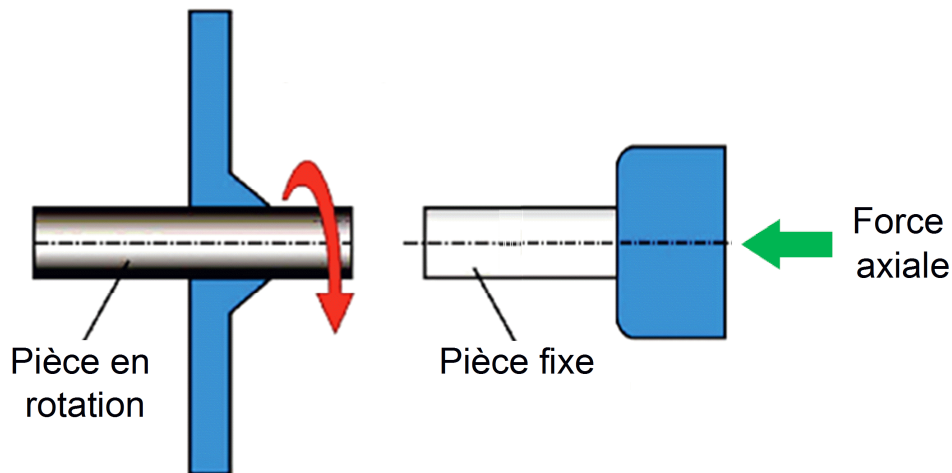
Principe de soudage par friction rotative [9].
